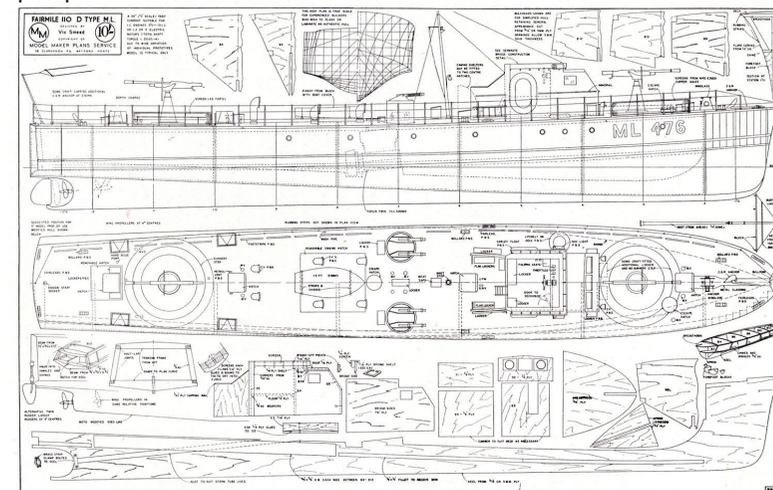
planimetria e componenti della Fairmile Patrol Boat.
